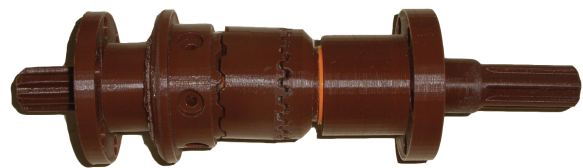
Модель редукторной вставки к винтовому насосу (корпус снят)
